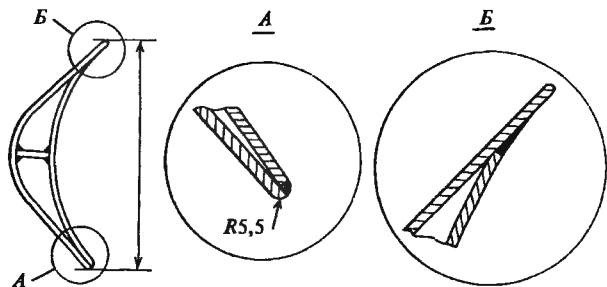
Сварно-штампованная сопловая лопатка ХТЗ (сечение лопатки)
